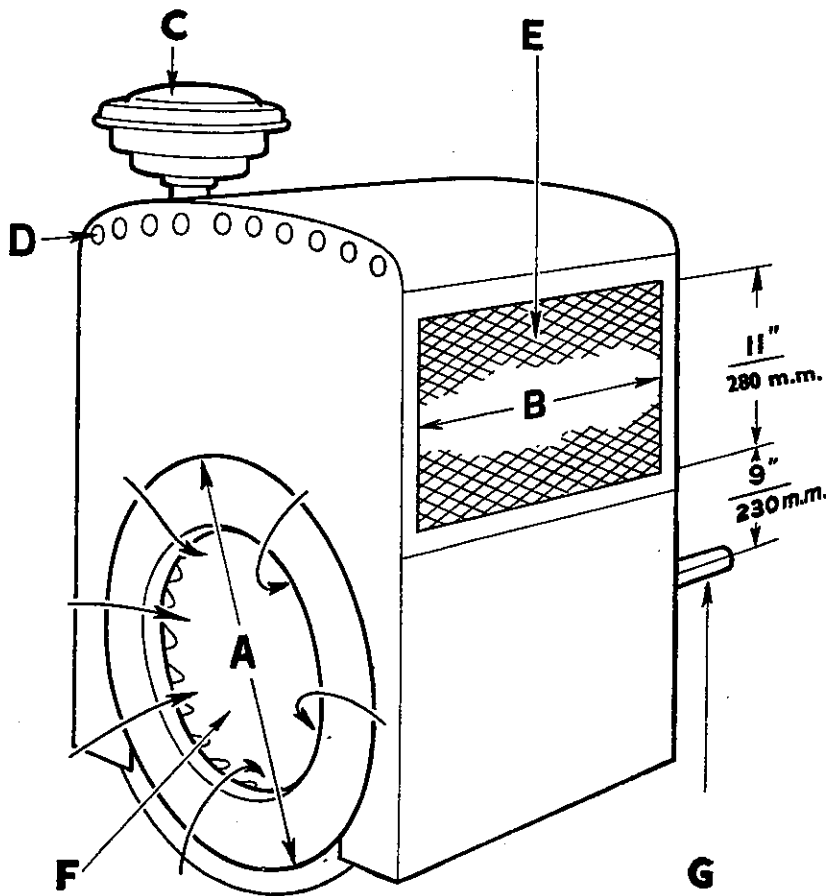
Motor in omkasting, het geheel opgesteld in de buitenlucht
